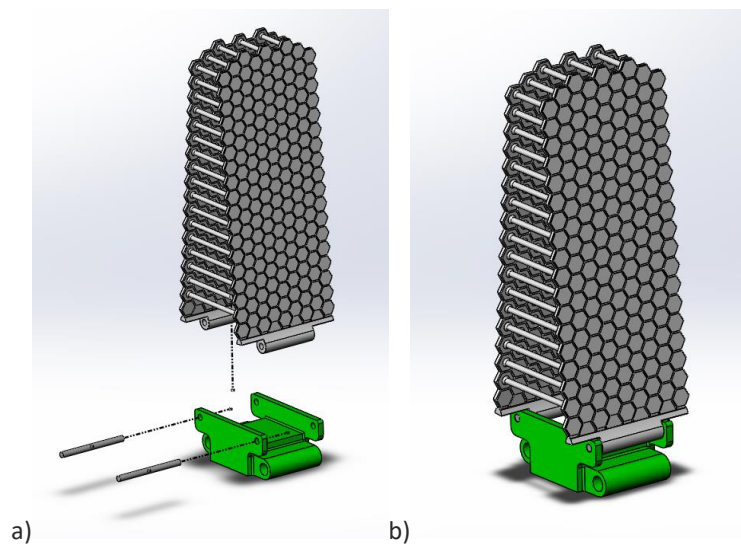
7ª parte da montagem - vista explodida da montagem (a) e parte da montagem completa (b).
